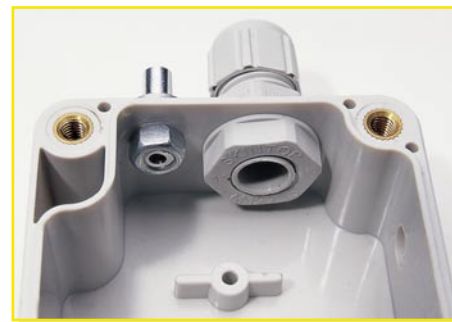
Detailansicht zur Montage der Kabeldurchführung und des Luftanschlusstutzens
